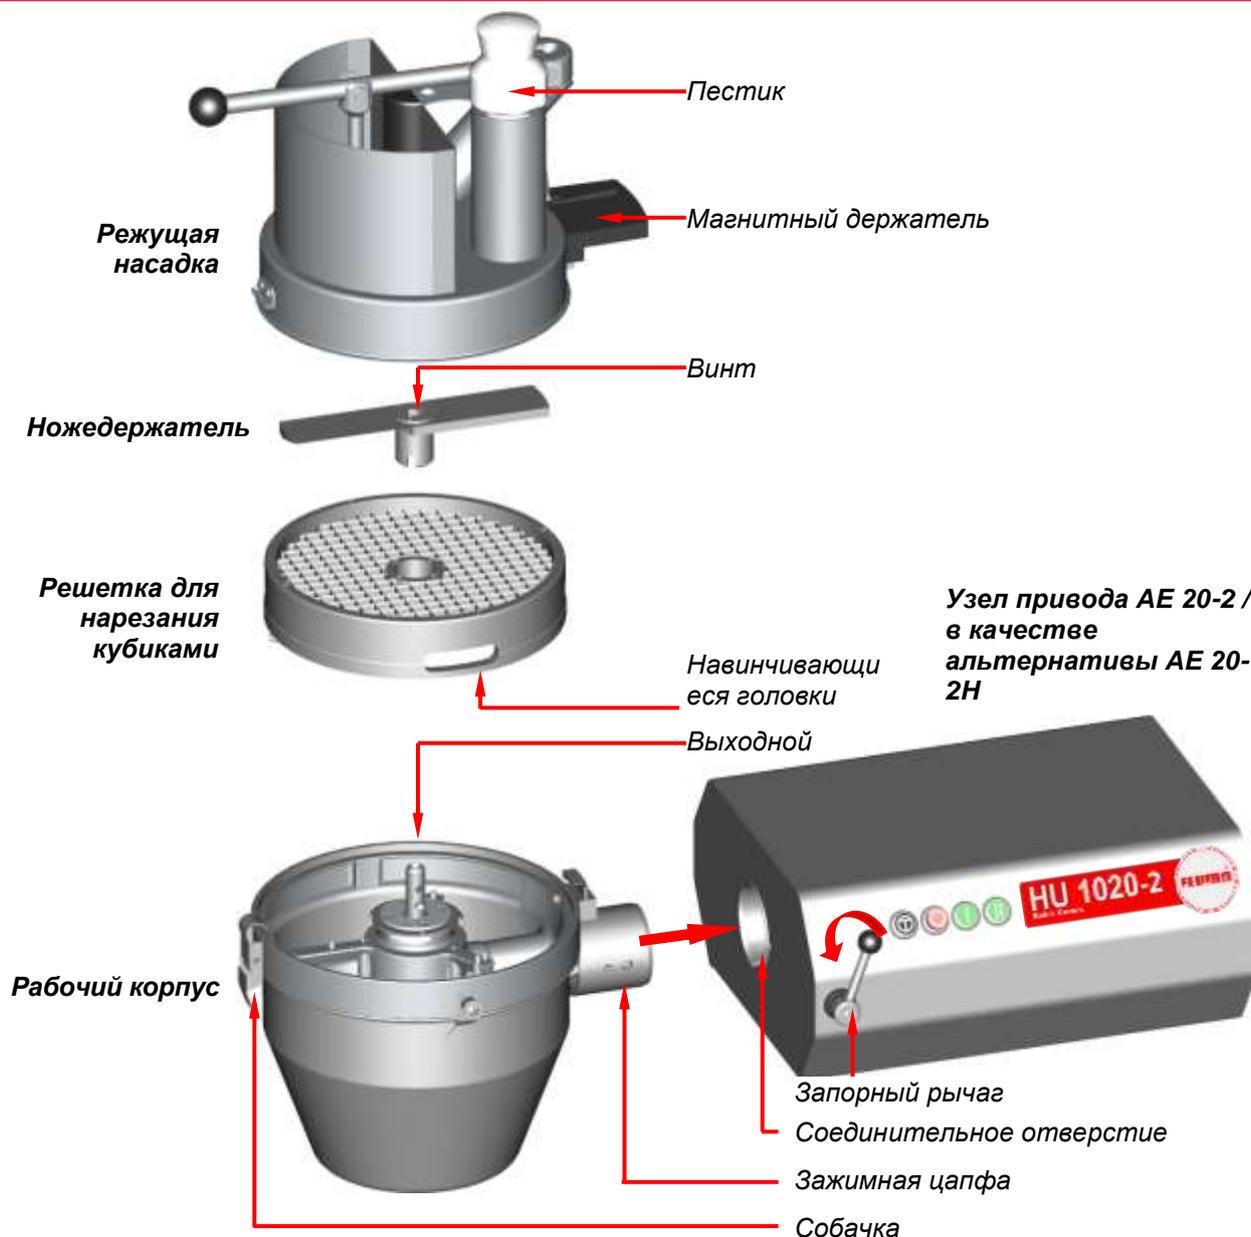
Режущая насадка, приспособление для нарезания кубиками, рабочий корпус и узел привода АЕ 20-2/АЕ 20-2Н
